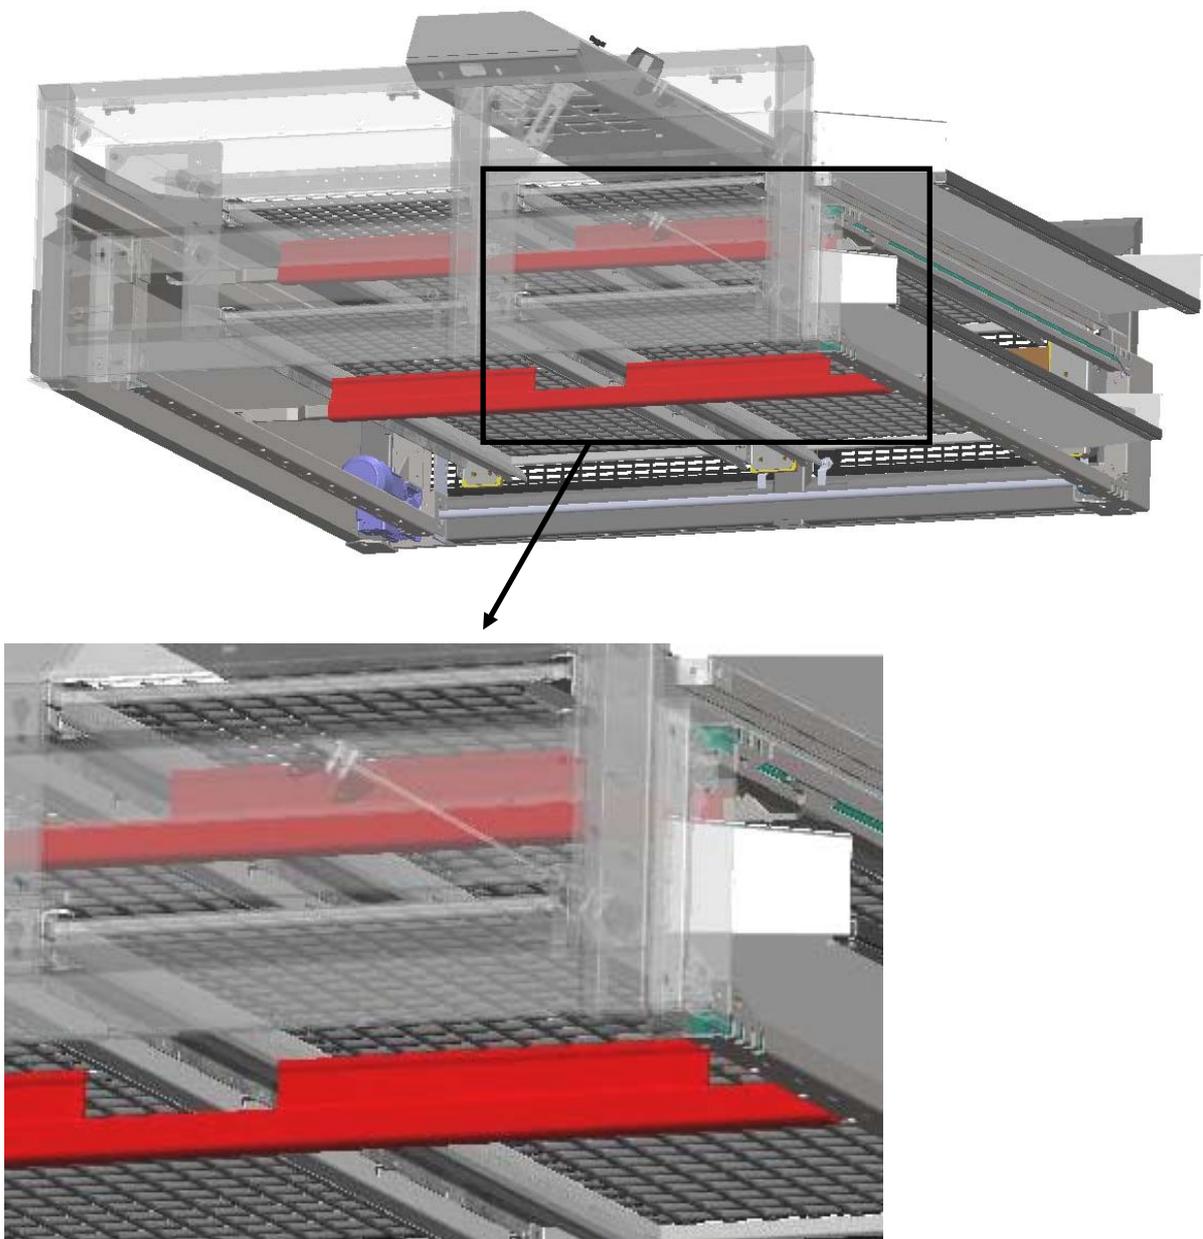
zeigt die Platzierung der „Spritzschläuche“, die die Siebe in ihrer Position im Siebkasten halten.
